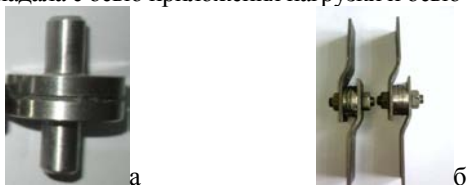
Образцы для испытаний на сдвиг (а -исходный, б –в приспособлении для испытания)
